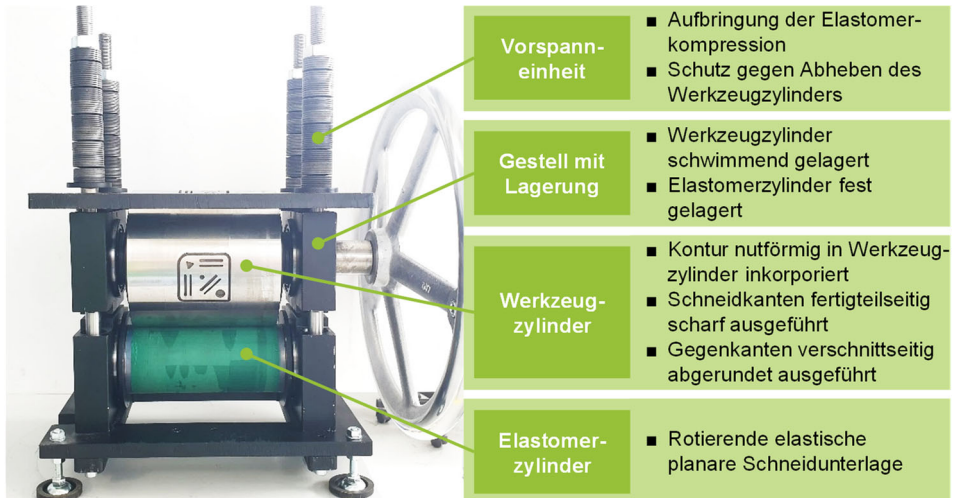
Prototypisches Schneidaggregat zum rotativen Elastomer-Schneiden
